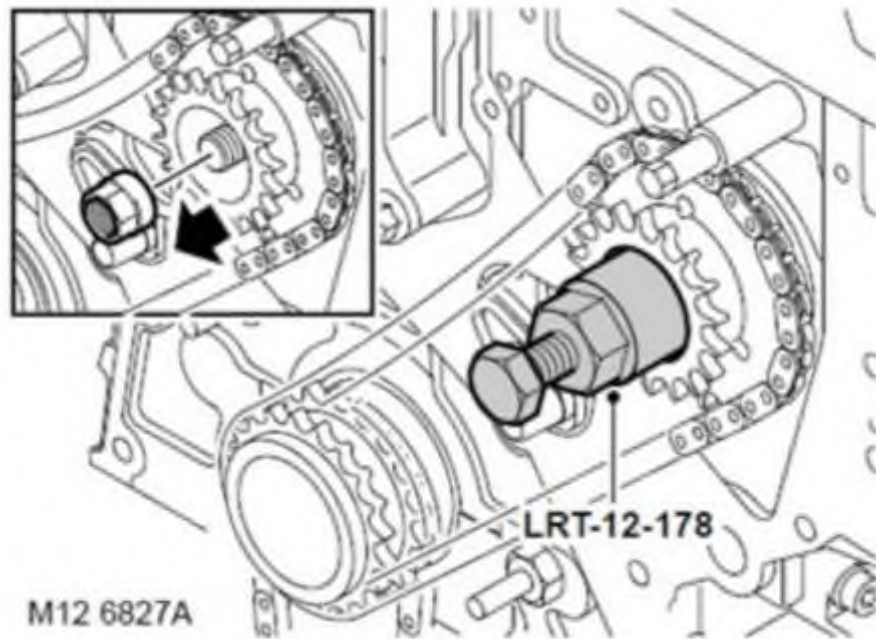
Демонтаж вала ПНВД з шестерні.
